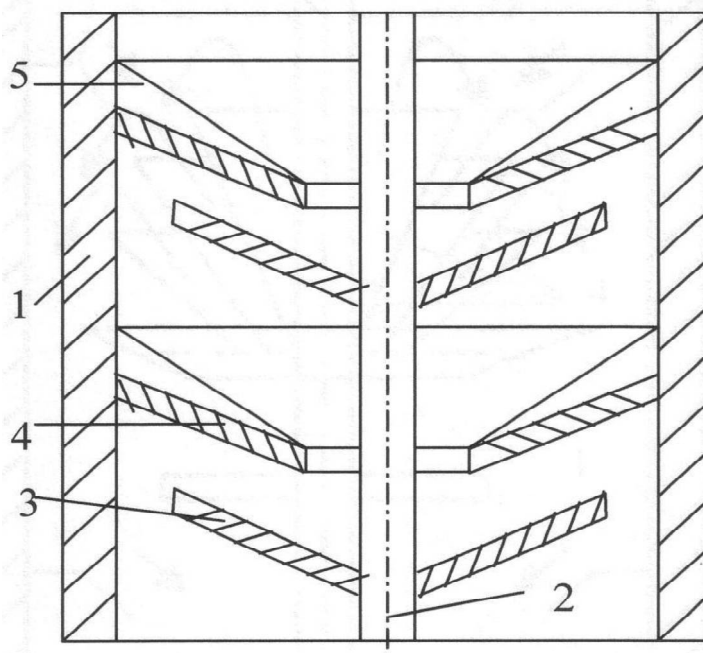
Усовершенствованная роторная колонна с распиливающими дисками: 1 - корпус; 2 - вал; 3 - распиливающий диск; 4 - неподвижная тарелка; 5 - перегородка.
